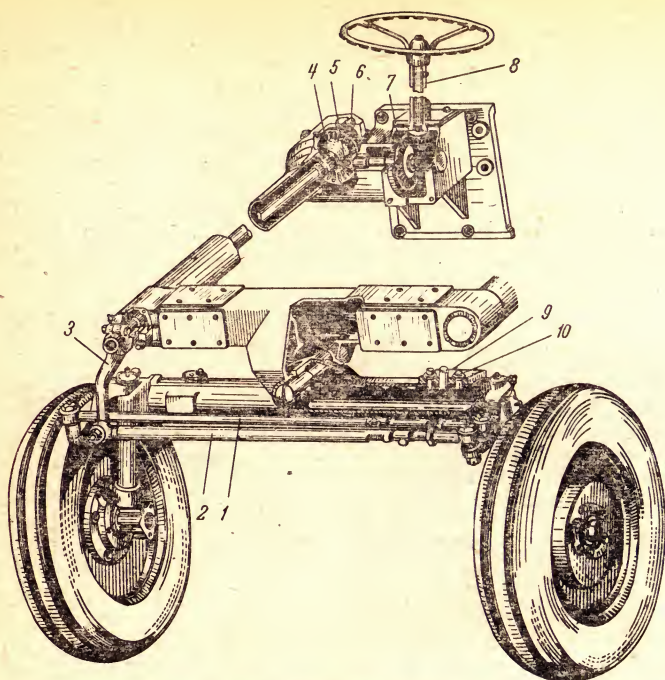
Регулировка колеи передних колес и механизма рулевого управления самоходного шасси Т-16М:
